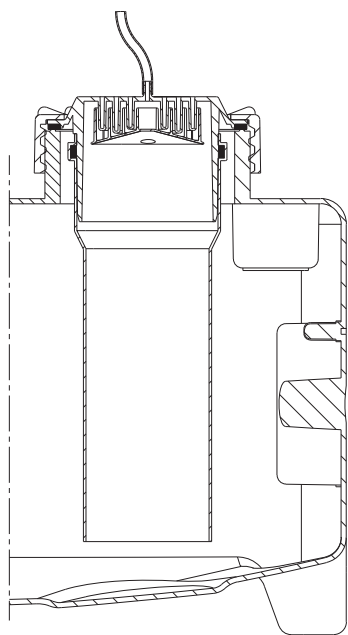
Крышка с резьбой и пневматическая трубка, трубка DN 100 и уловитель конденсата
